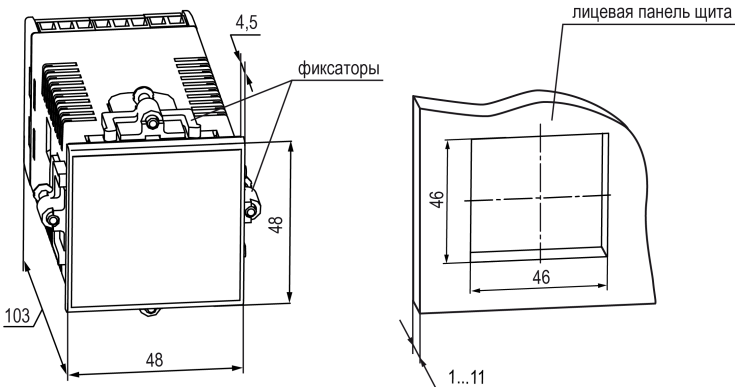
Габаритные размеры корпуса Щ5 и монтажного отверстия в щите
